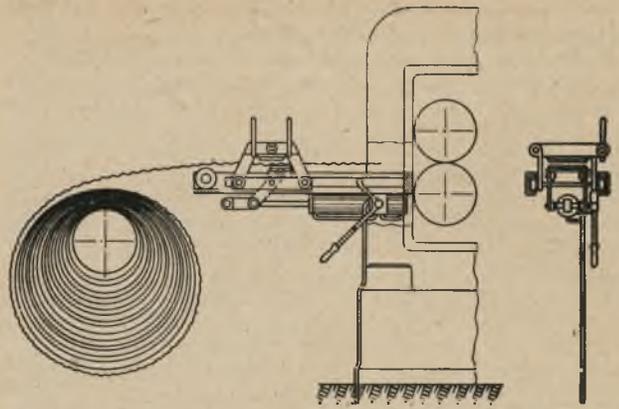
Einstoßvorrichtung und Bandpresse an einer Kaltwalzmaschine.
